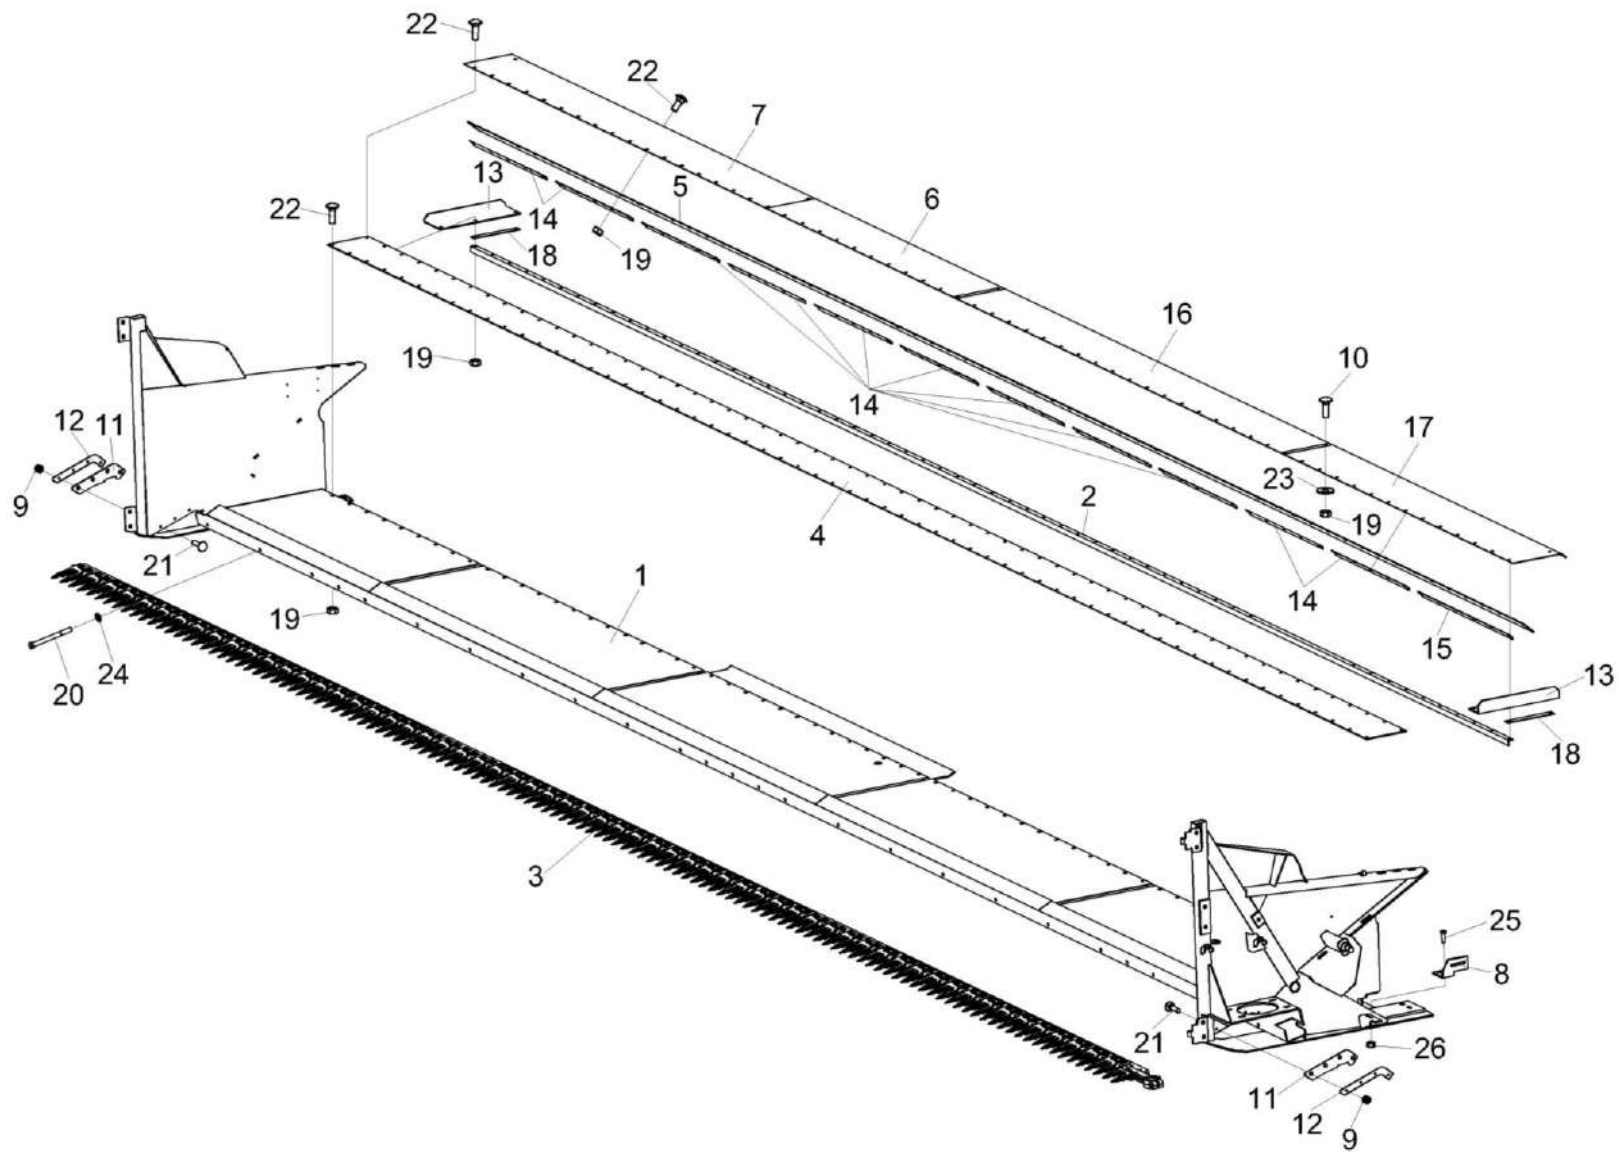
Приспособление для уборки рапса КЗК-9-1-1540000 (лист 2)
